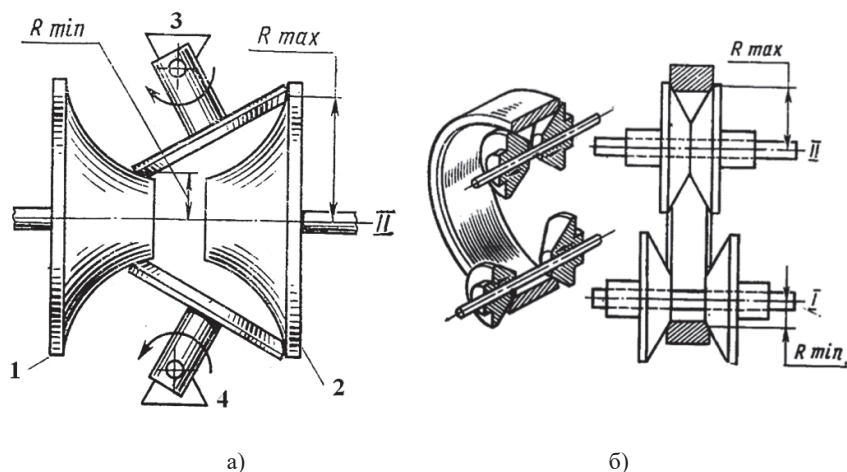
Схемы вариаторов с соосными и параллельными приводными валами
